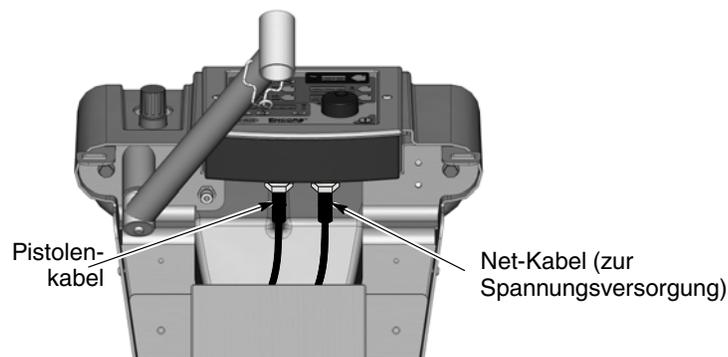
Pistolenkabel am Schnittstellenmodul anschließen - mobile Systeme
